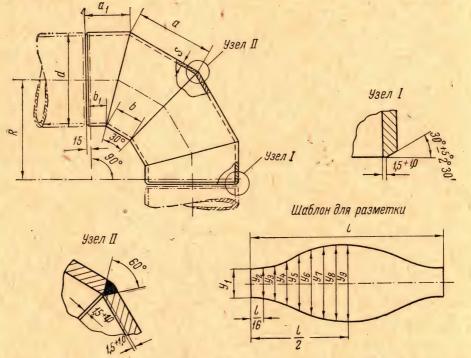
Отвод сварной с углом поворота 90°.
